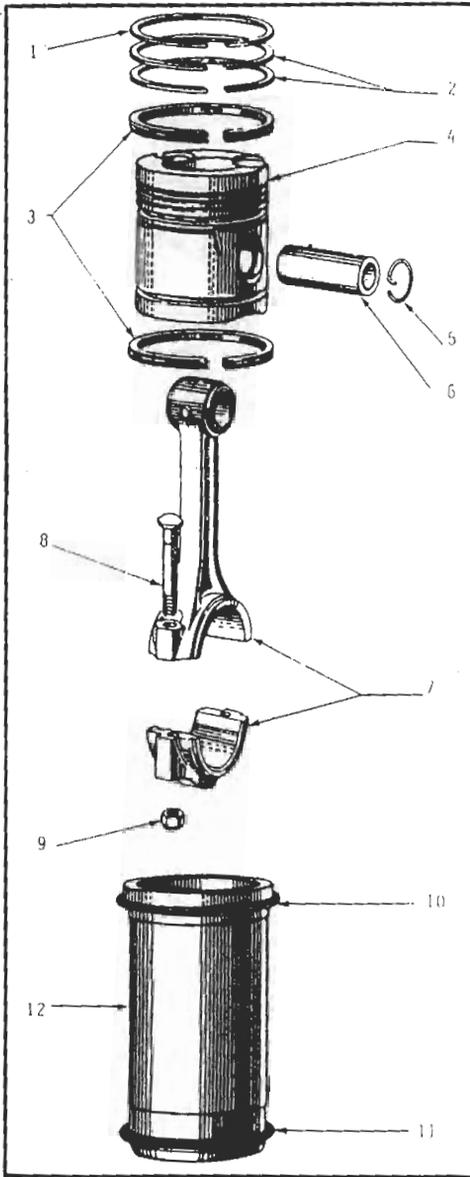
Conjunto de cilindro, émbolo, segmentos y biela (FORD). 1.- Segmento de fuego. 2.- Segmentos de compresión. 3.- Segmentos de engrase o rascadores. 4.- Émbolo o pistón. 5.- Clip o frenillo. 6.- Bulón. 7.- Cabeza y sombrerete de biela. 8.- Perno. 9.- Tuerca. 10 y 11.- Anillos de caucho. 12.- Cilindro.
